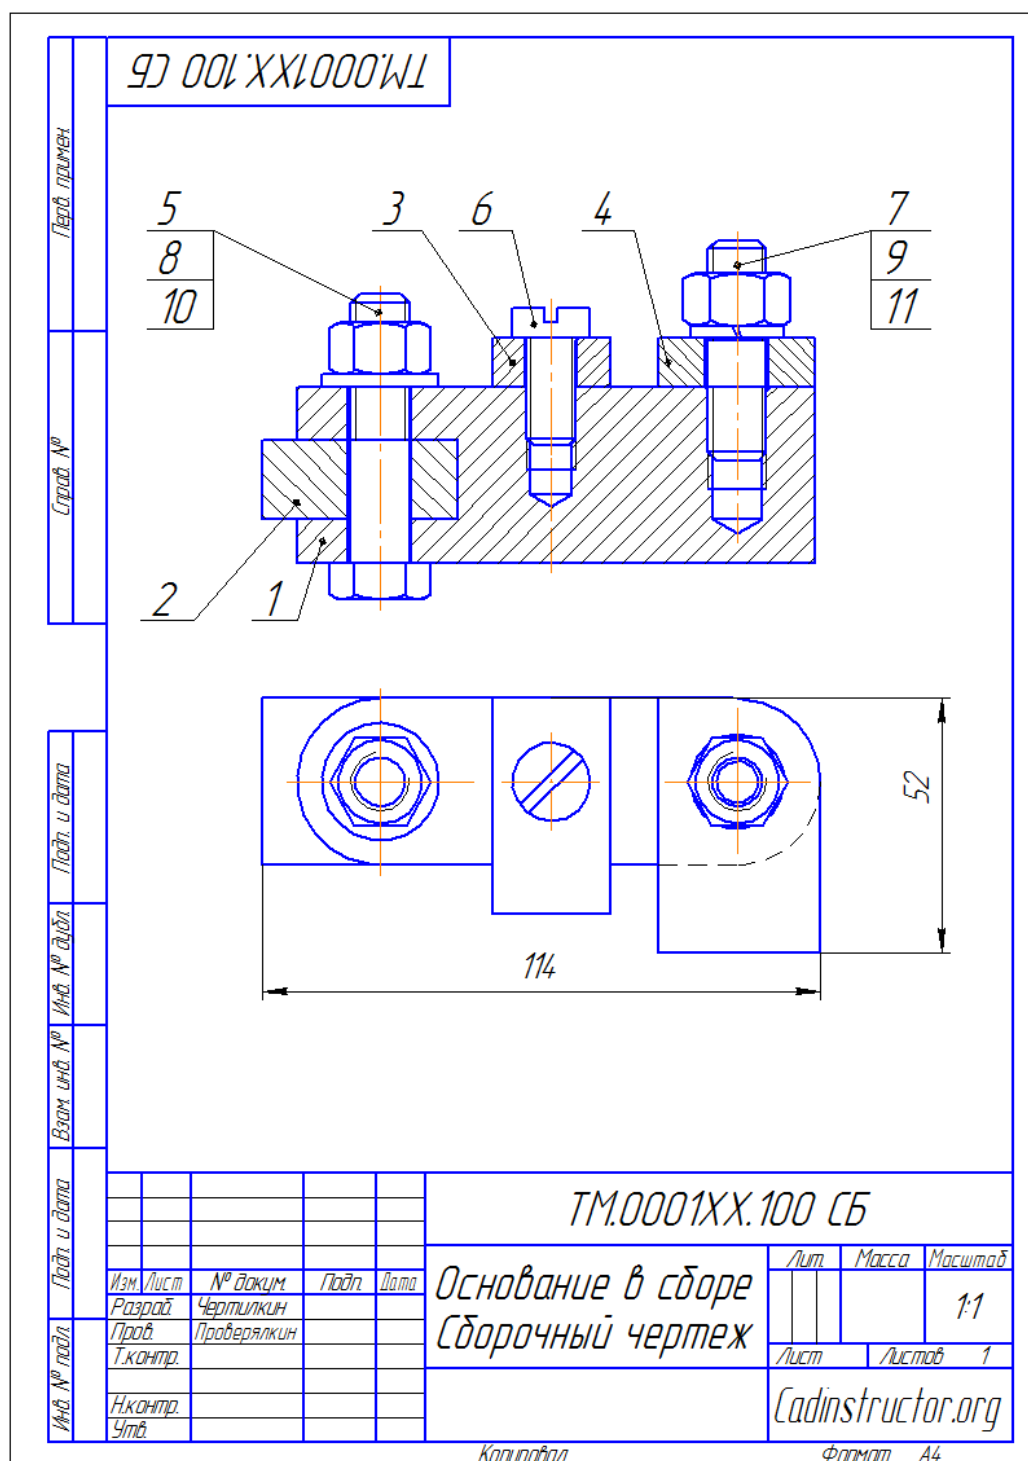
Пример выполнения лабораторной работы по теме «Резьбовые соединения». Сборочный чертеж
